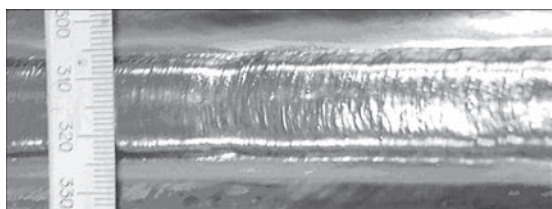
Характер формирования поверхности металла, наплавленного порошковой проволокой ППТ-22 на пластину сплава ВТ22
